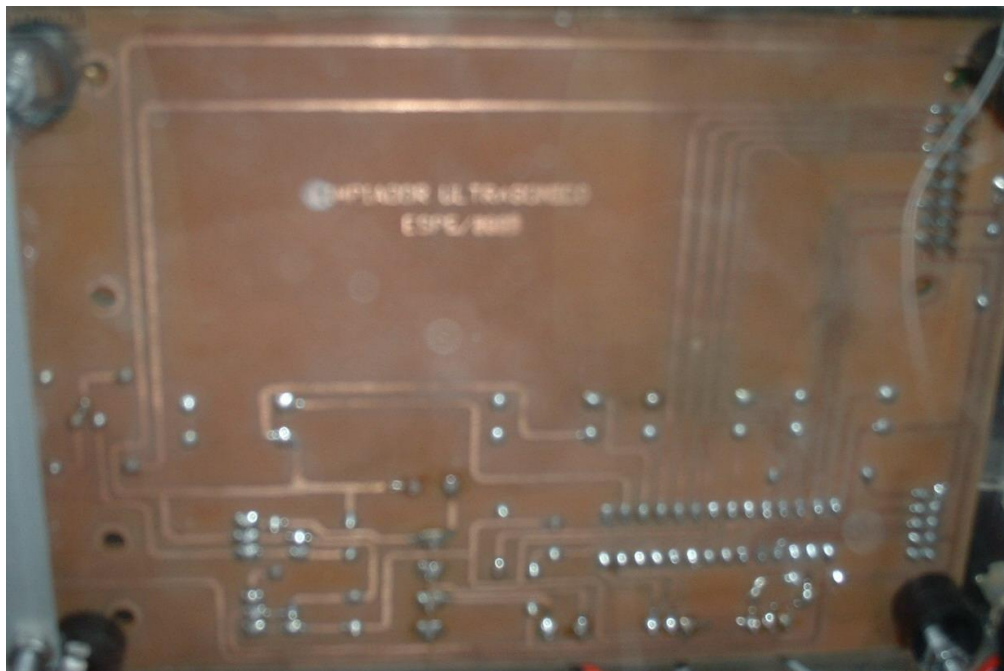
Placa PCB de la tarjeta de control y pantalla LCD.
